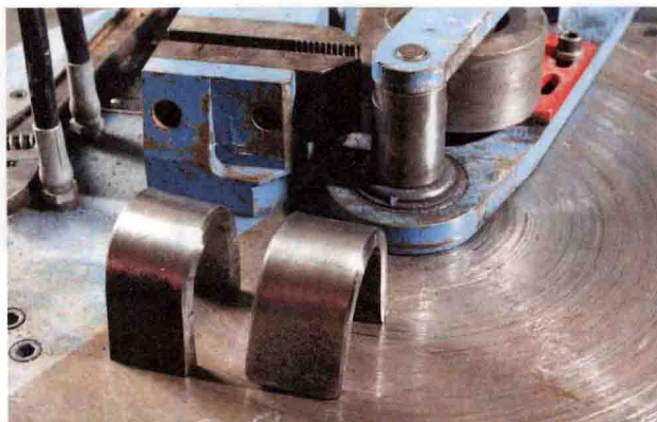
当缠绕弯曲试验机完成一个循环时，取下弯曲试样并目测检查是否符合所用的焊接规程中的标准。应对两个工件进行弯曲试验，一个是焊缝正面弯曲试验(焊缝的顶面)，另一个是焊缝根部弯曲试验(焊缝的底面)。
